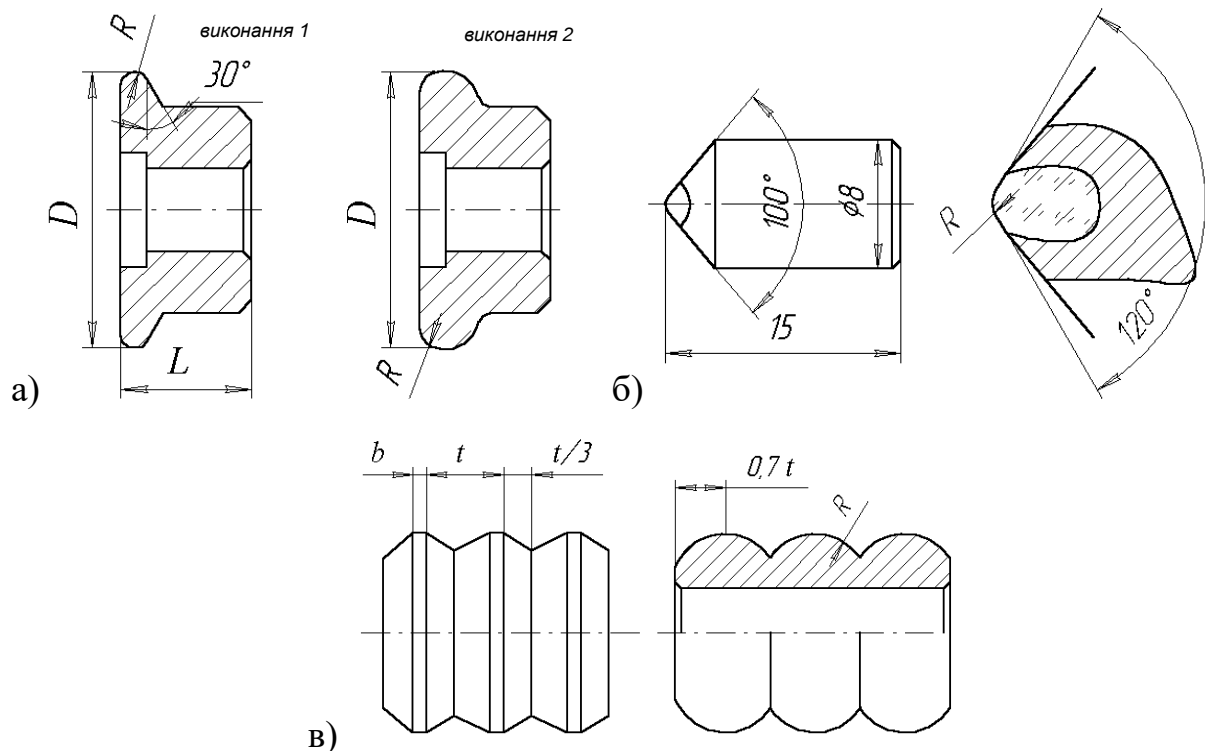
Ролики для зміцнювальної обкатки поверхонь (а); алмазний наконечник для вигладжування поверхонь (б); деформуючі частини протяжок (в)
